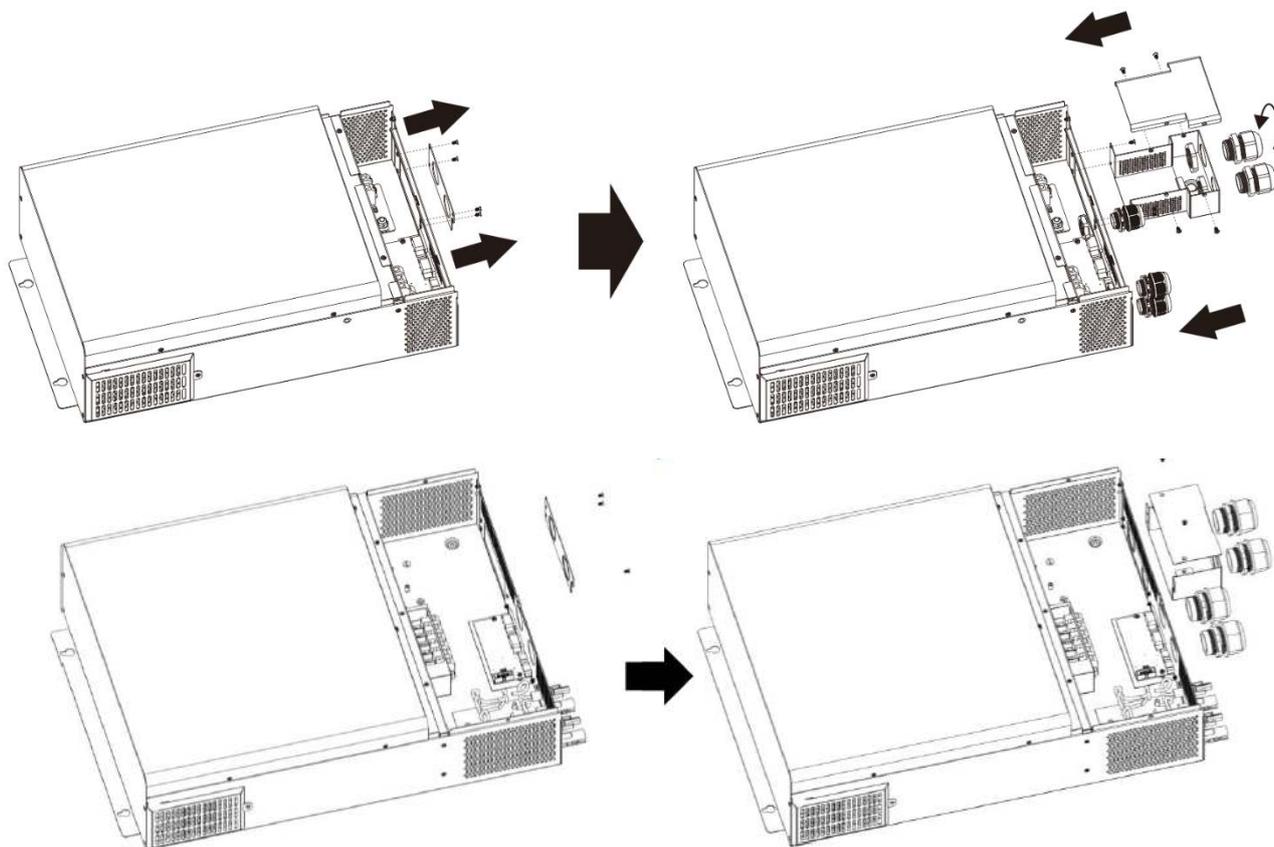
Installation des presse-étoupes et du boîtier d'extension du câblage de la batterie (PSW-H-3KW-120/24V et PSW-H-6.5KW-120/48V)
